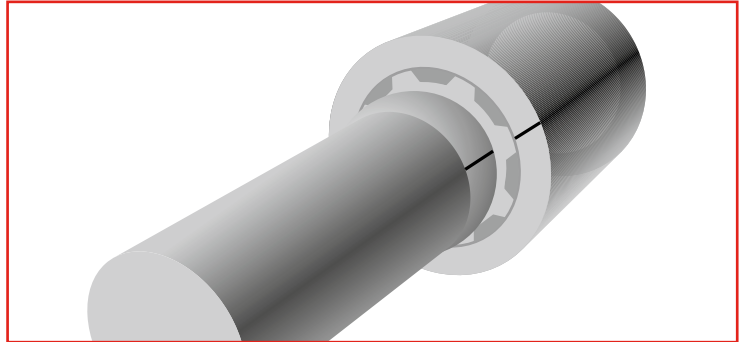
Marque la posición de la flecha estriada en el casquillo para un ensamble en el futuro.
